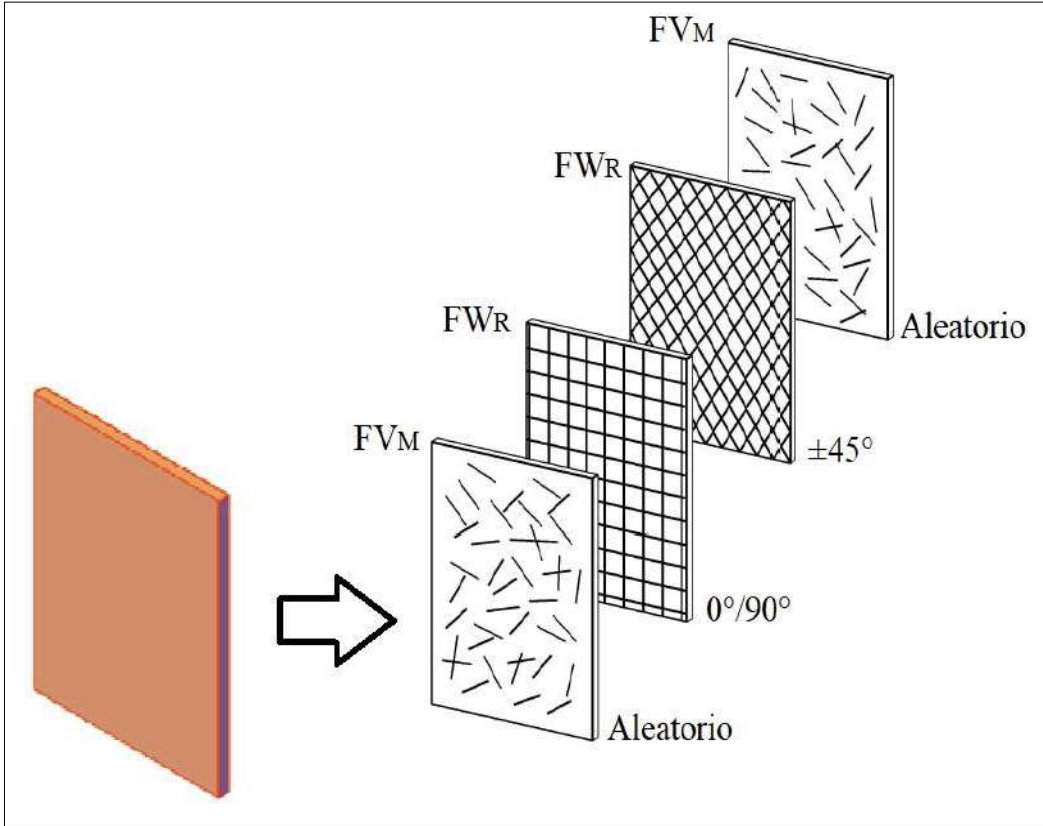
Esquema del Laminado Propuesto 3 (Lp3)
